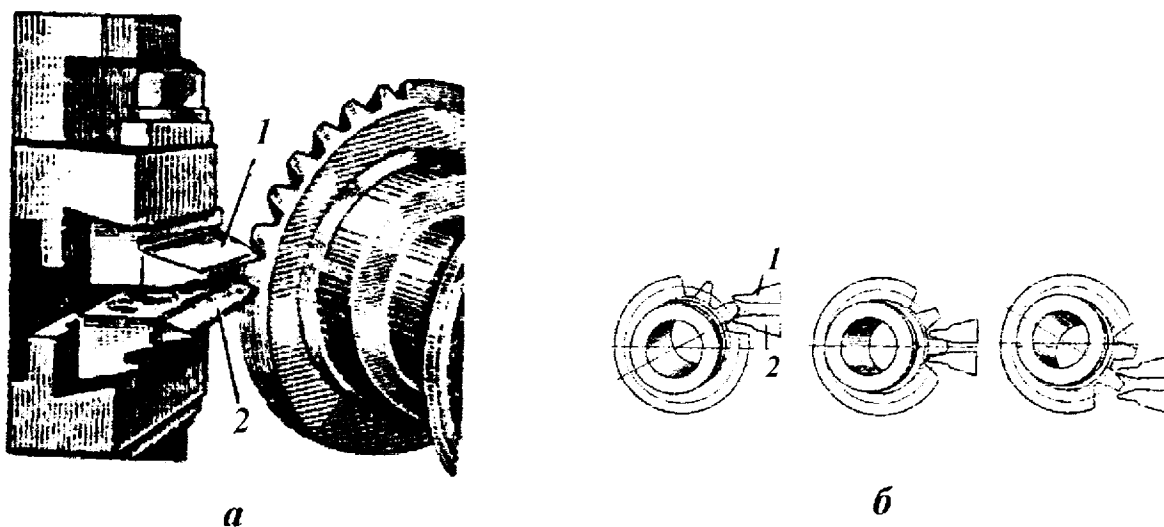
Нарезание конического зубчатого колеса на зубострогальном станке: а – установка резцов; б – схема обкатки; 1 и 2 – резцы
